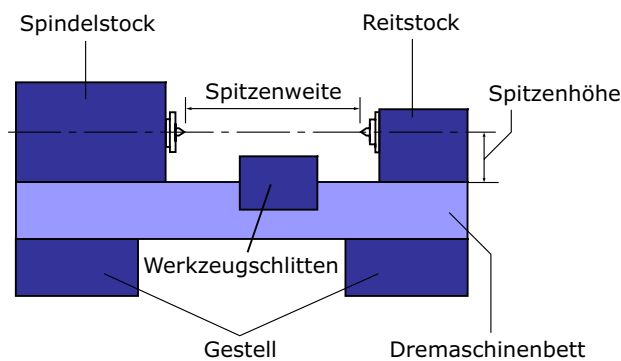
reZ) Aufbau einer Drehbank: Das Werkstück wird zwischen Spindelstock und Reitstock eingespannt, der Drehmeissel ist auf dem Werkzeugschlitten befestigt.
